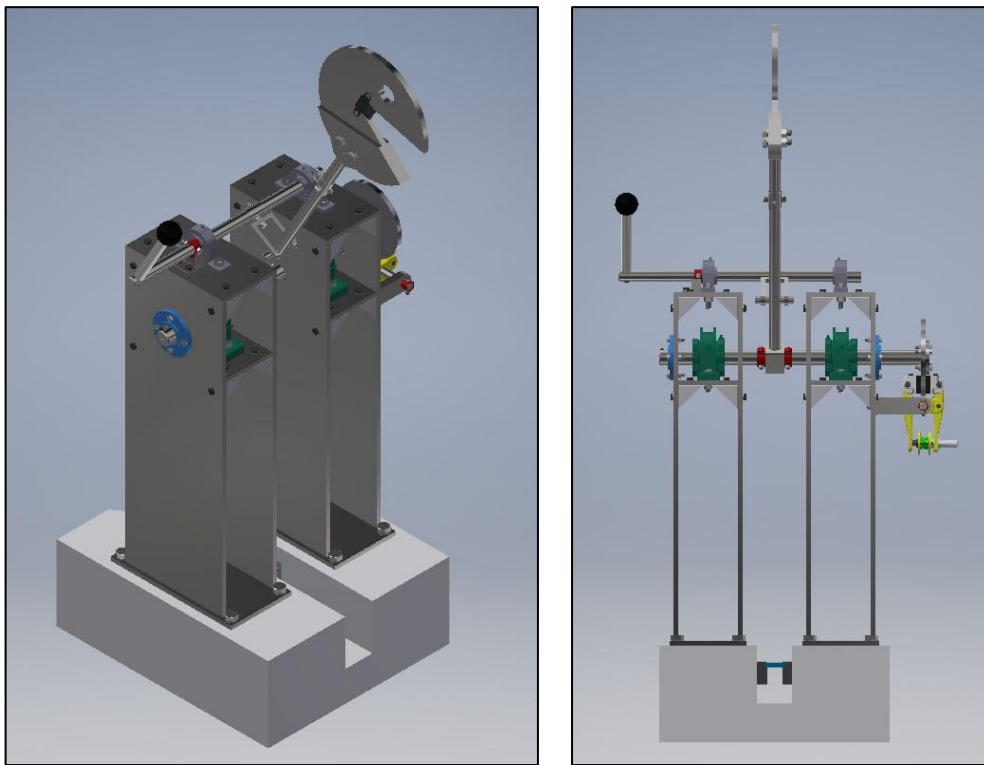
Diseño final con vista en perspectiva (izquierda) y frontal (derecha).
